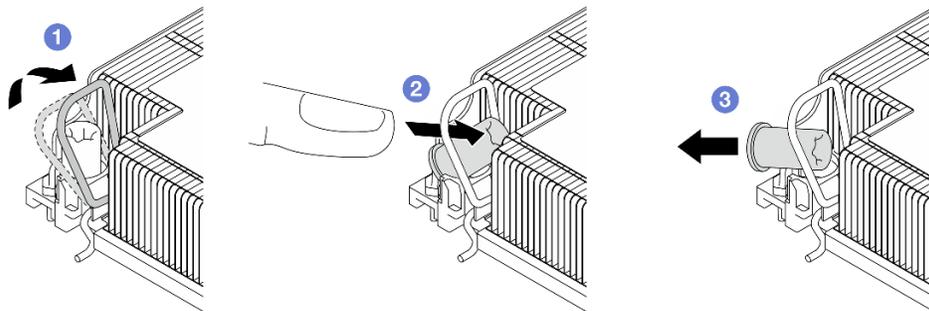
Entfernen einer T30-Torx-Mutter vom Kühlkörper
